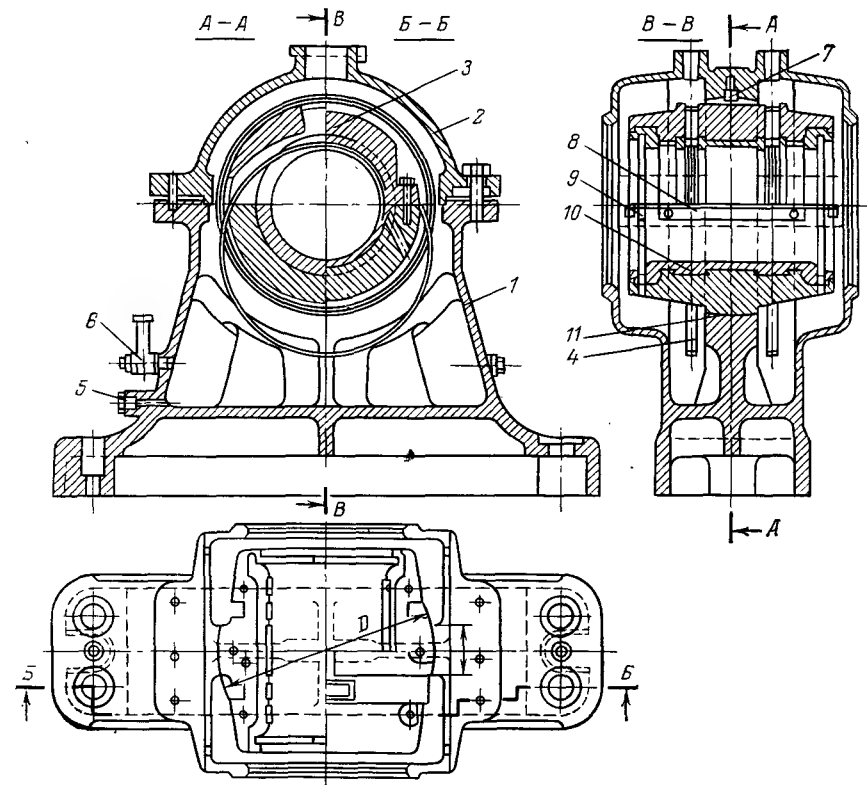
Стоячковый подшипник с кольцевой смазкой
